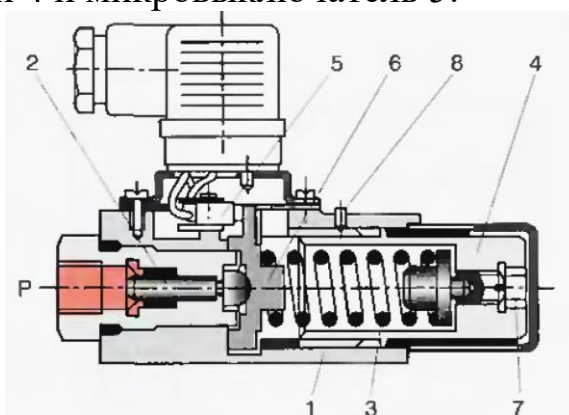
Конструкция реле давления плунжерного типа компактного исполнения
